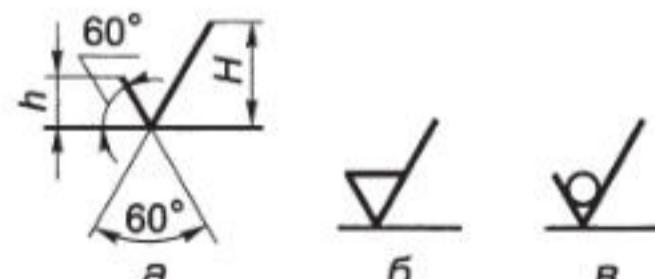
Варианты знаков в обозначении шероховатости поверхности:
